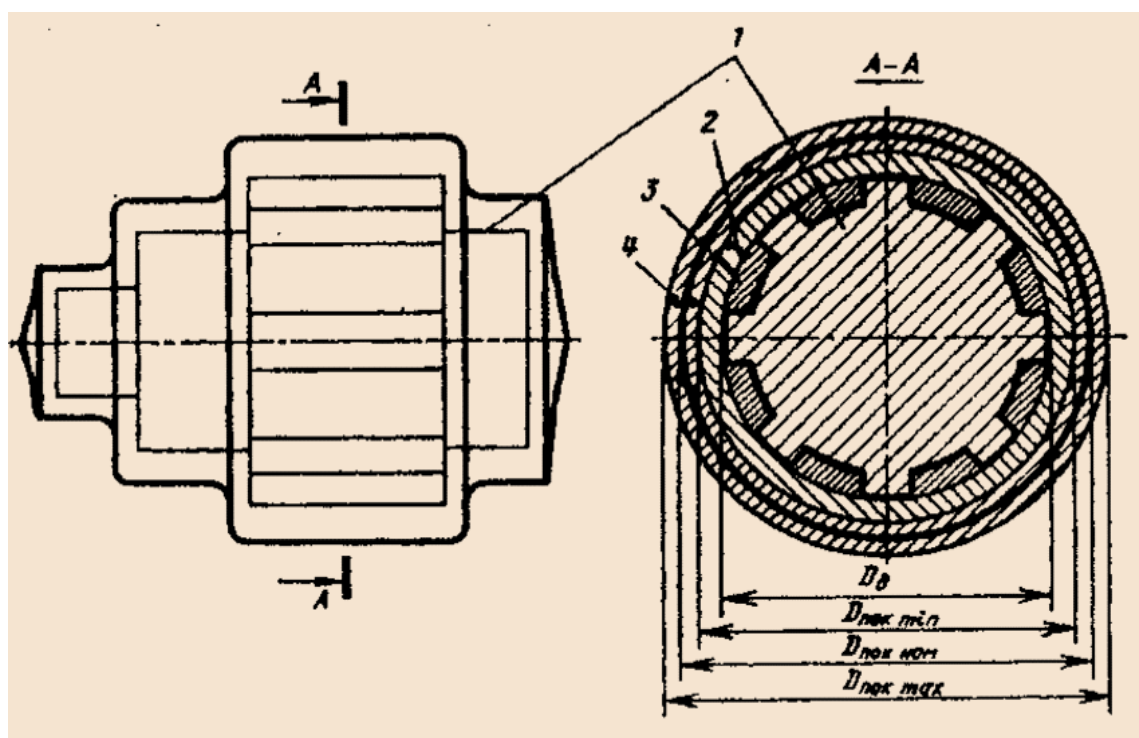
Схема размеров поковки с напуском, припуском и допуском
